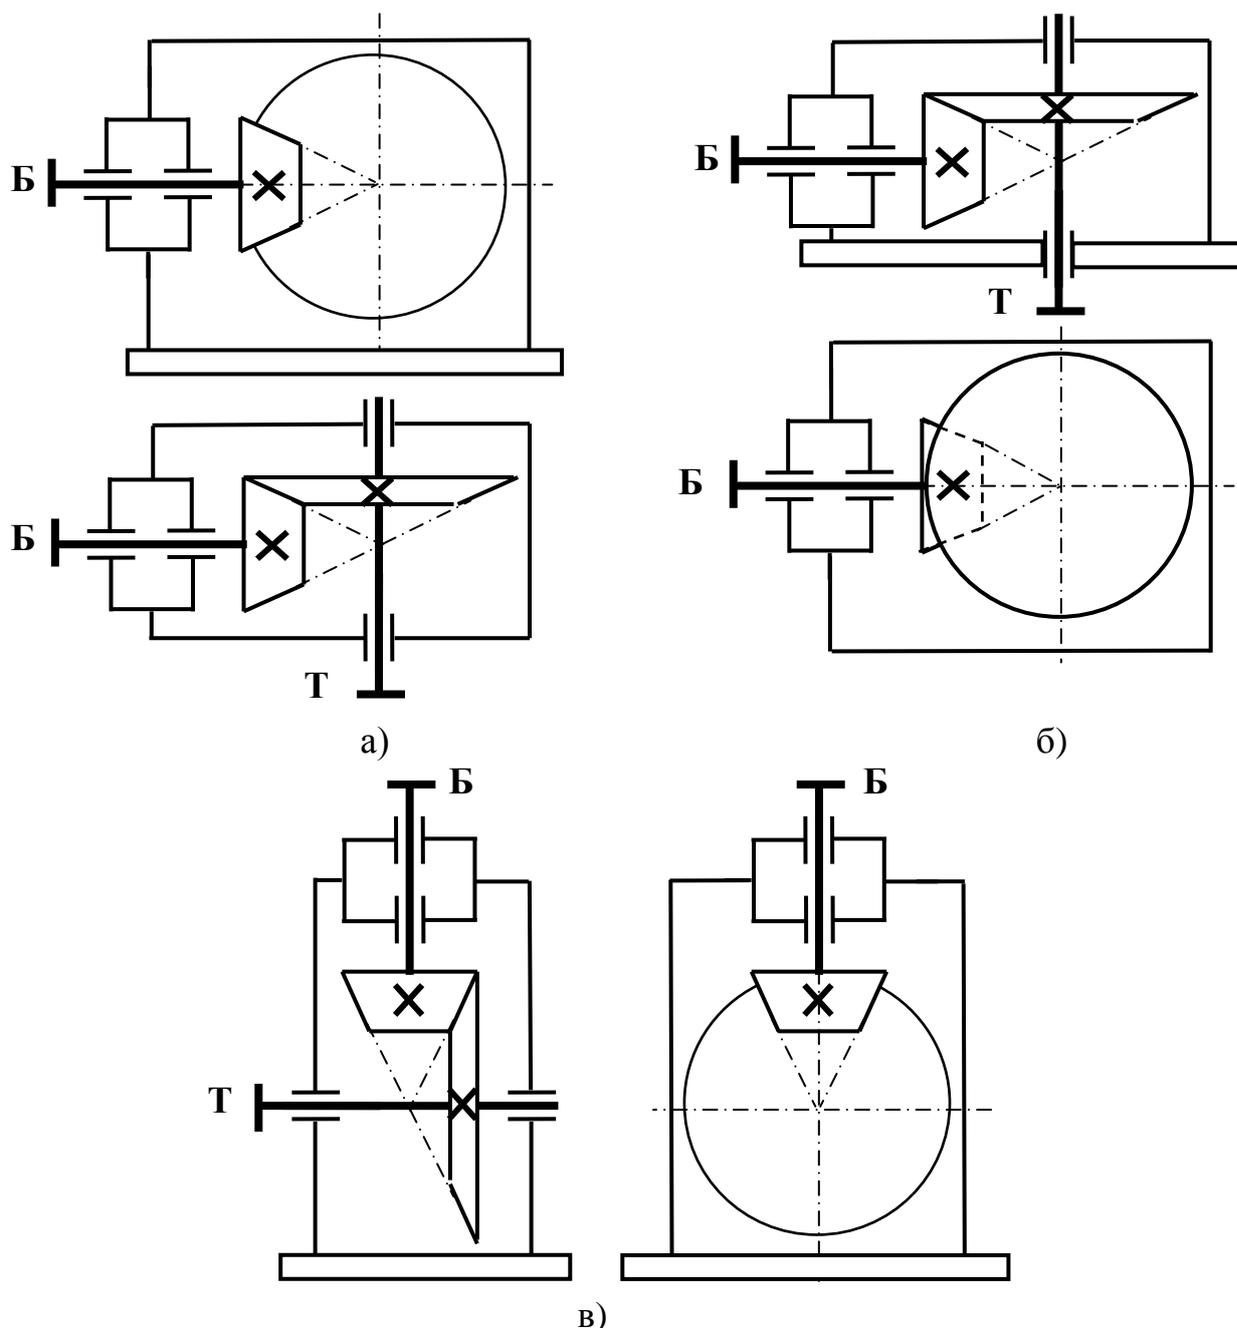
Основные кинематические схемы одноступенчатых конических редукторов
